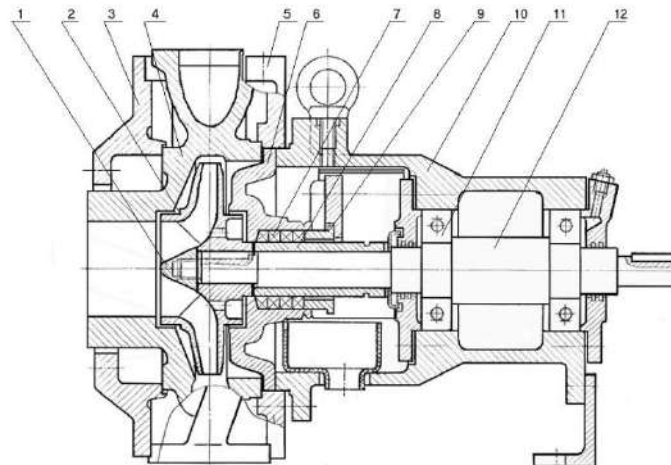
Продольный разрез центробежного насоса: 1 – гайка рабочего колеса, 2 – колесо рабочее, 3, 5 – прижимные фланцы, 4 – корпус насоса, 6 – корпус сальника, 7 – набивка сальника, 8 – защитная втулка, 9 – крышка сальника, 10 – кронштейн, 11 – подшипник, 12 – вал
